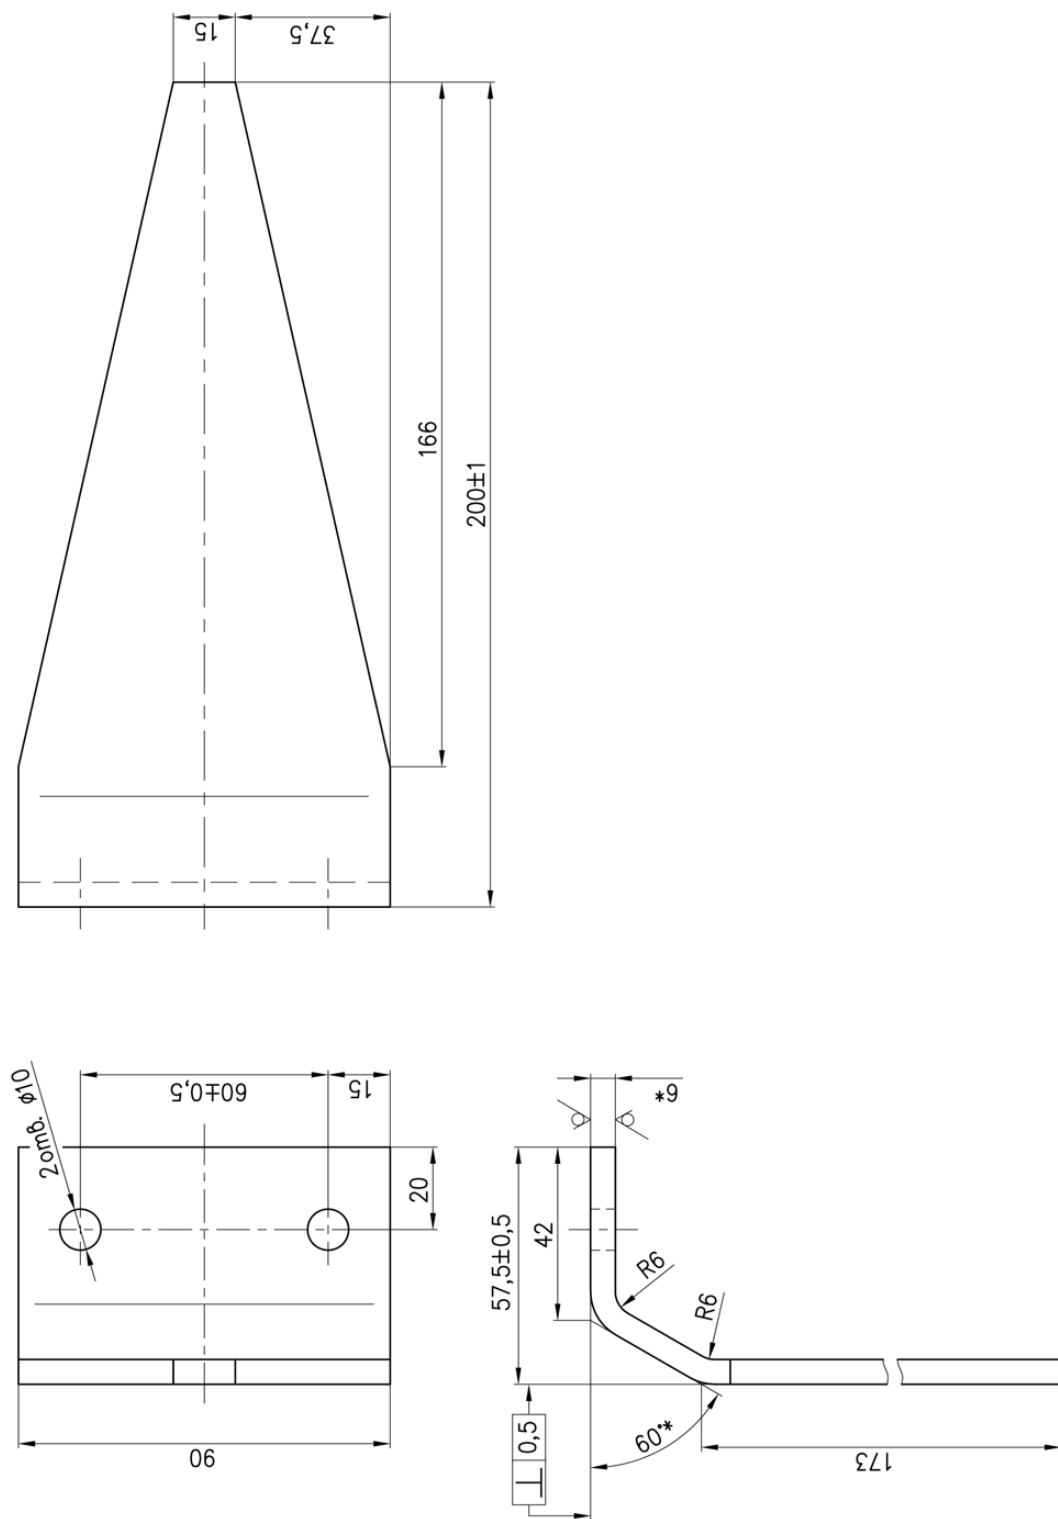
Фланец индуктора для установки ИИС 80-60
